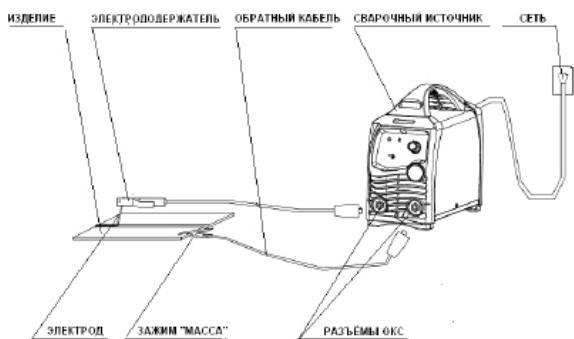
Схема подключения оборудования для MMA сварки
